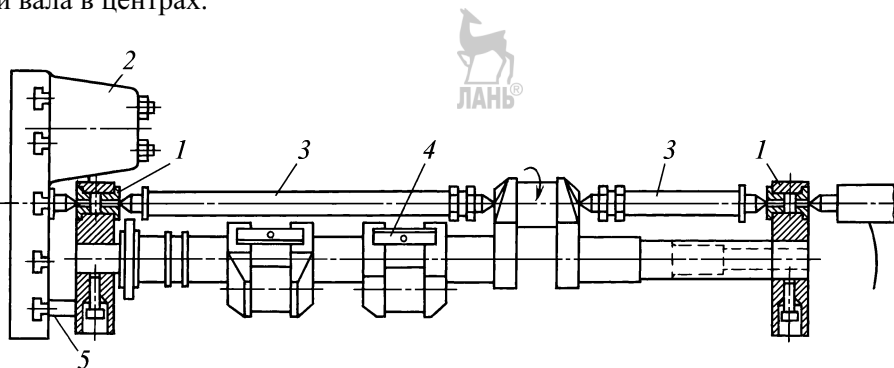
Схема обтачивания шатунных шеек на токарном станке:
